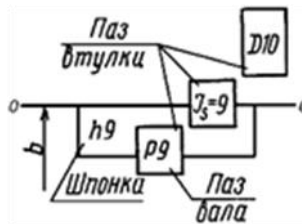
Поля допусков для ширины призматической шпонки, паза вала и втулки
